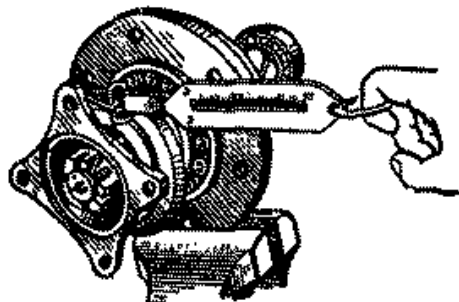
Проверка затяжки подшипников ведущей шестерни
